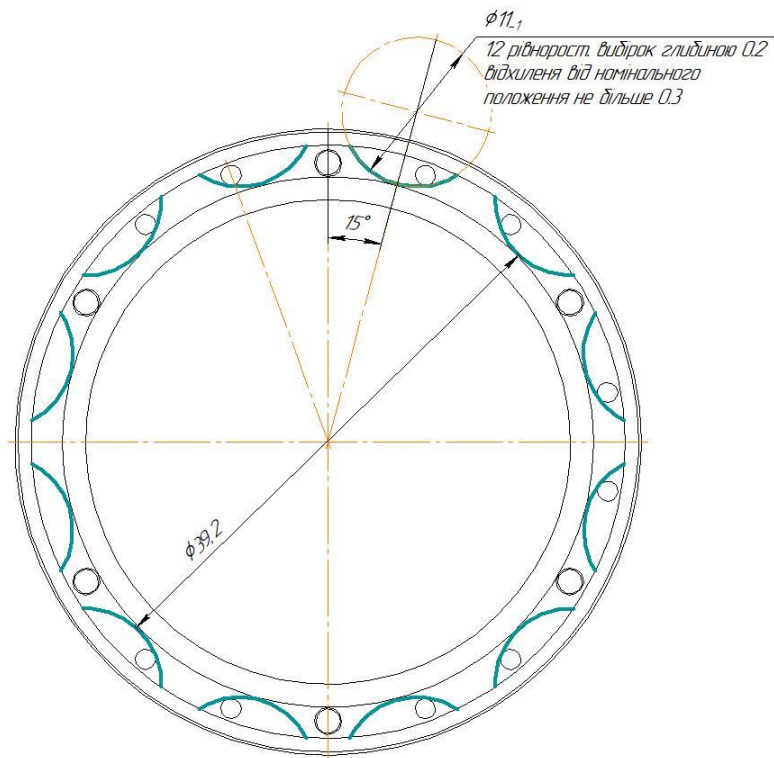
Операційний ескіз Фрезерної з ЧПК.
